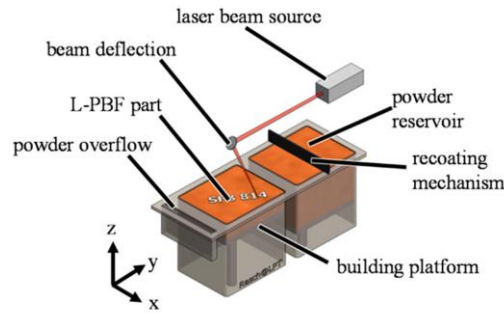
Disegno raffigurante il processo di Laser Powder Bed Fusion [69]
